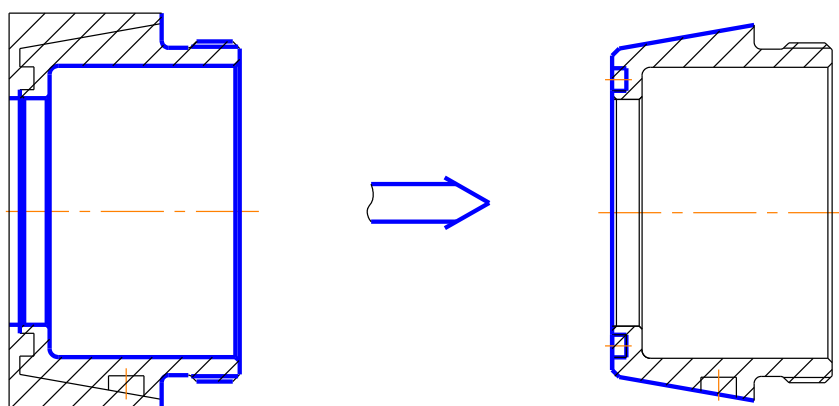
Перевстановлення заготовки при обробці з іншого боку на іншій шпindelній бабці
